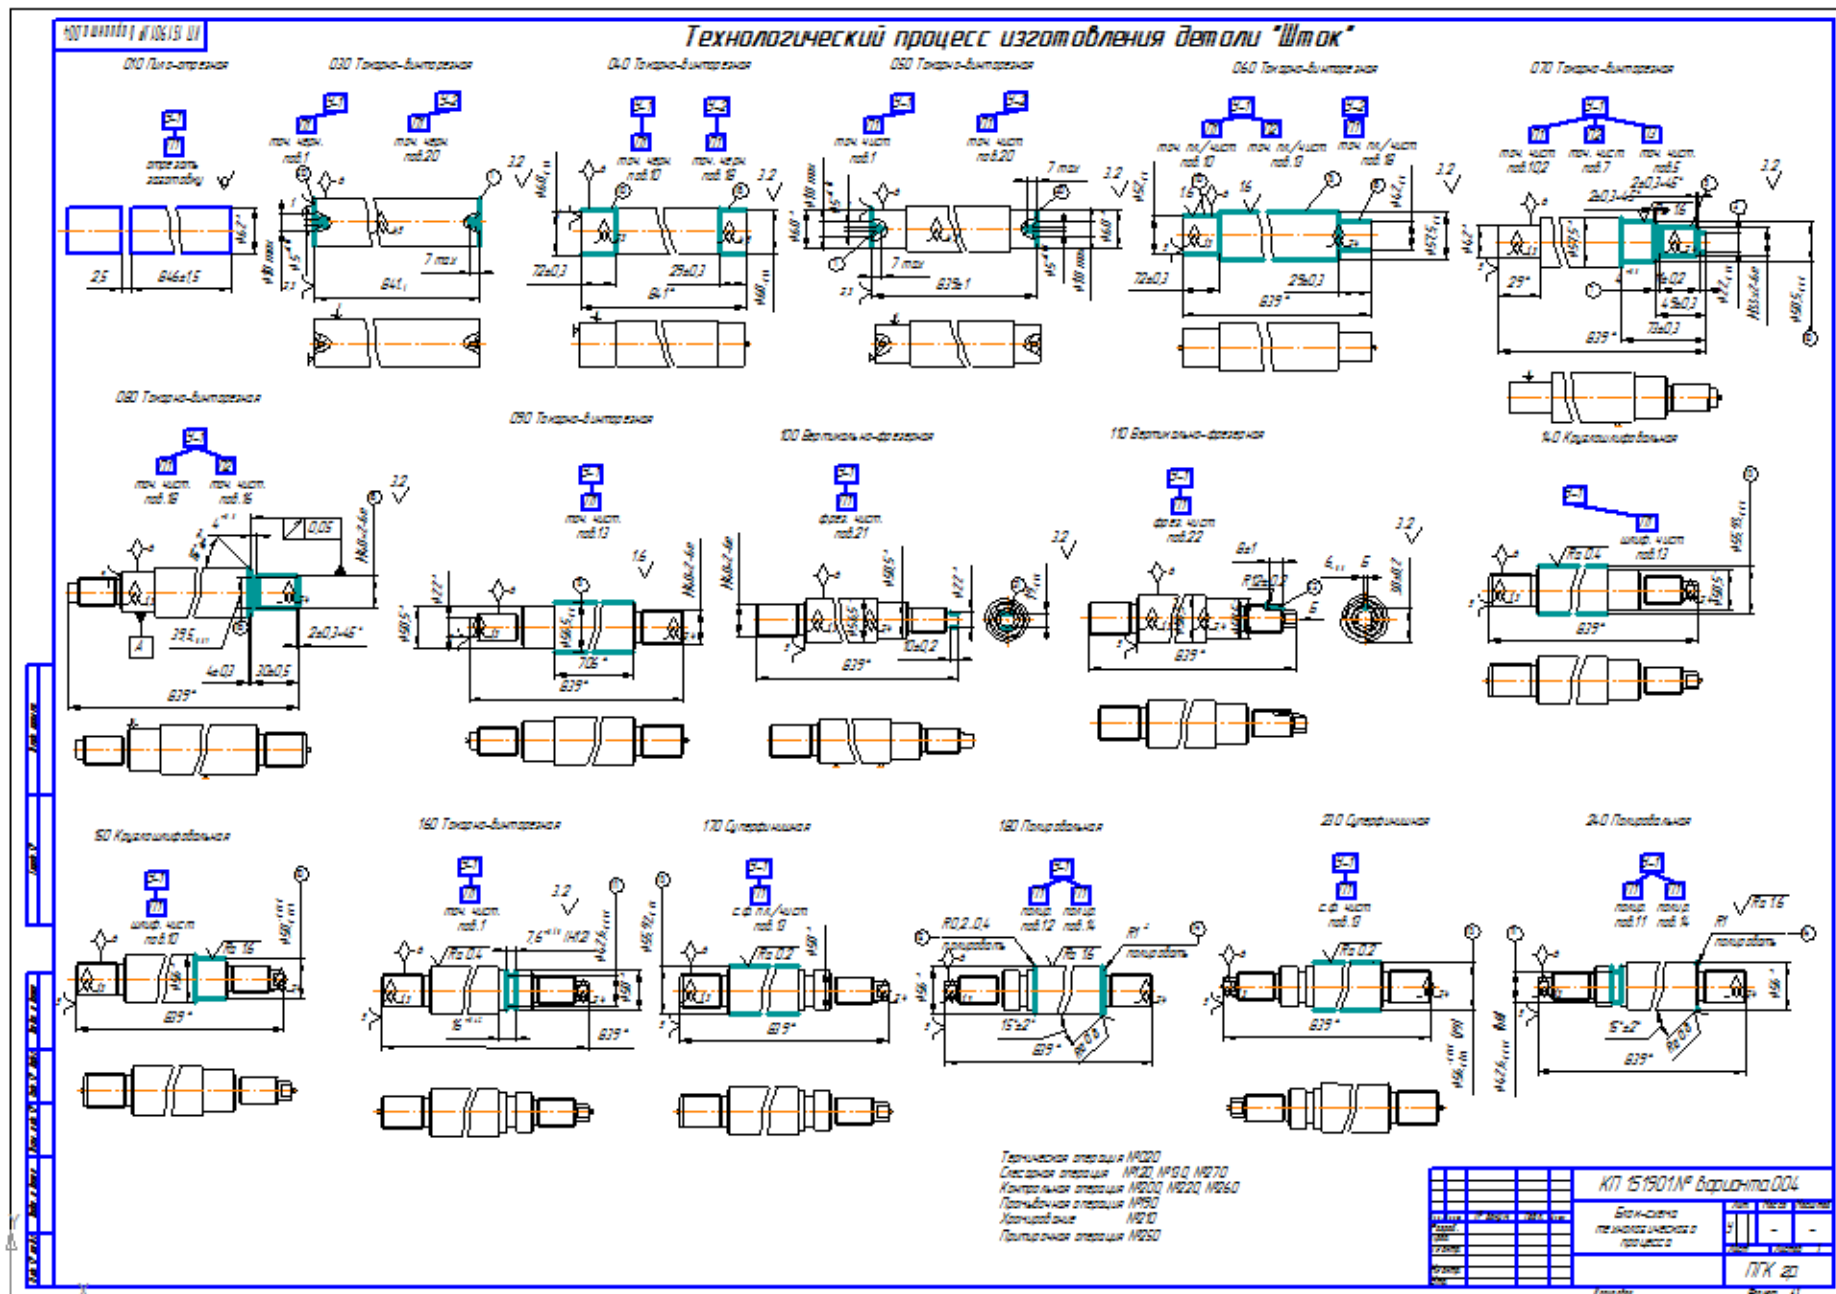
Технологический процесс изготовления детали «Шток».
